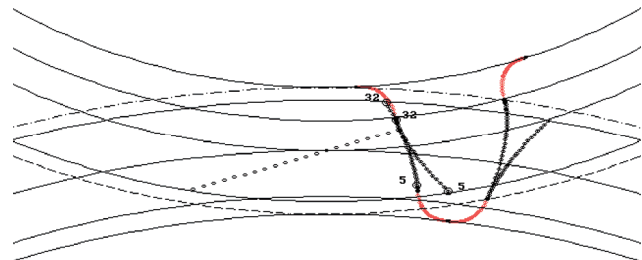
Зацепление профилей боковых поверхностей зубьев зубчатых колес с  $m = 5$ ,  $z_1 = 20$  и  $z_2 = 30$ , образованных инструментальной рейкой с прямолинейным профилем боковых поверхностей зубьев
